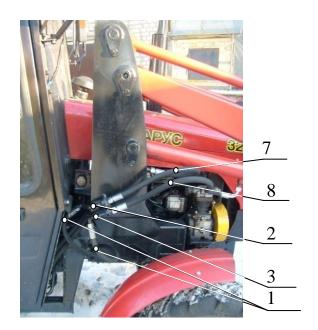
Установка РВД стреловых гидроцилиндров.
